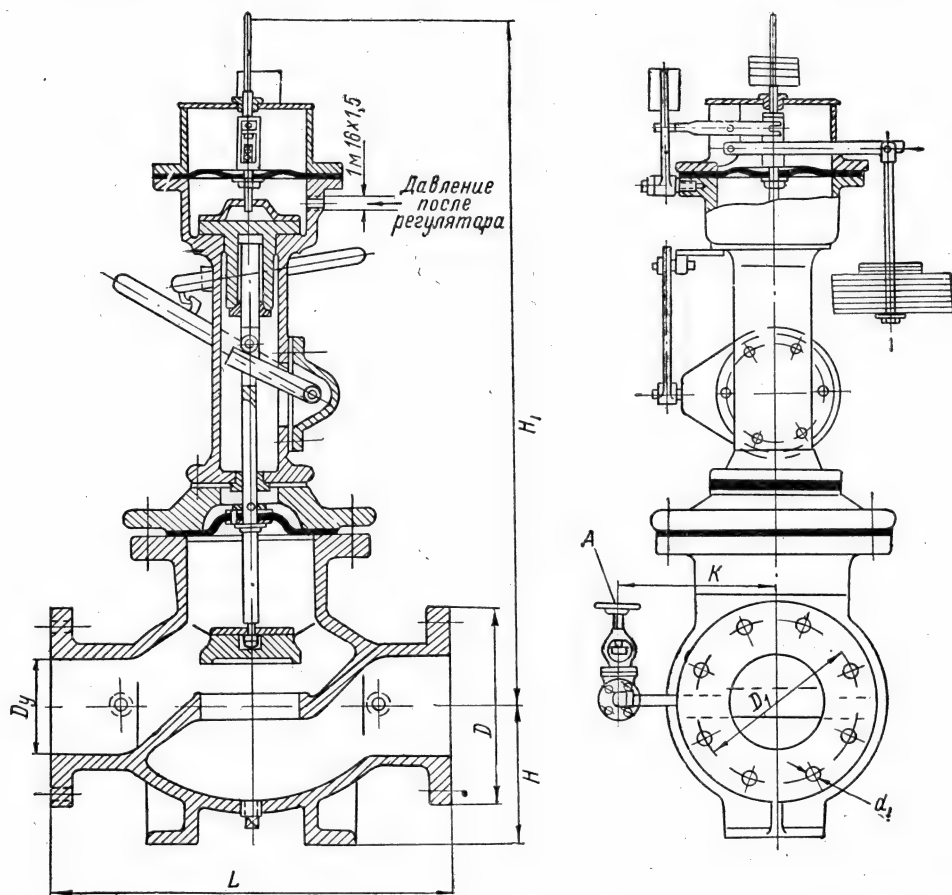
Предохранительный запорный клапан типа ПК-150, ПК-200 и ПК-300:
